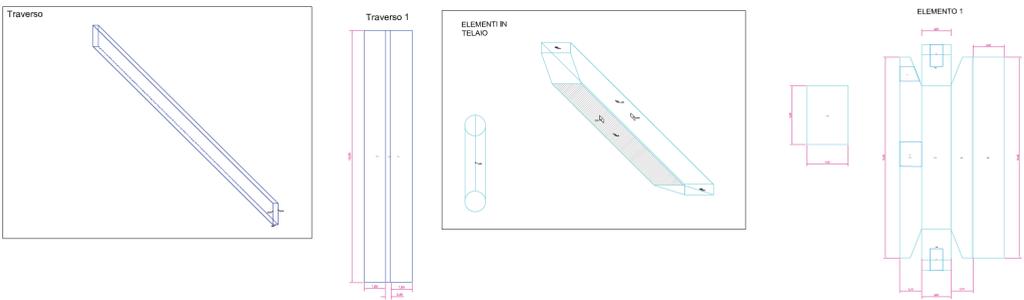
Elementi estratti dal modello 3D e loro sviluppo.
